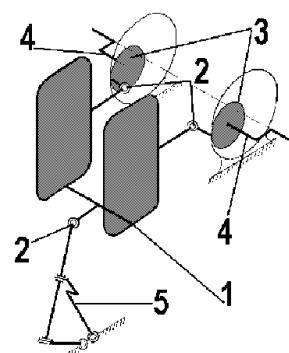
Малогабаритный приводной механизм перемещения клети
